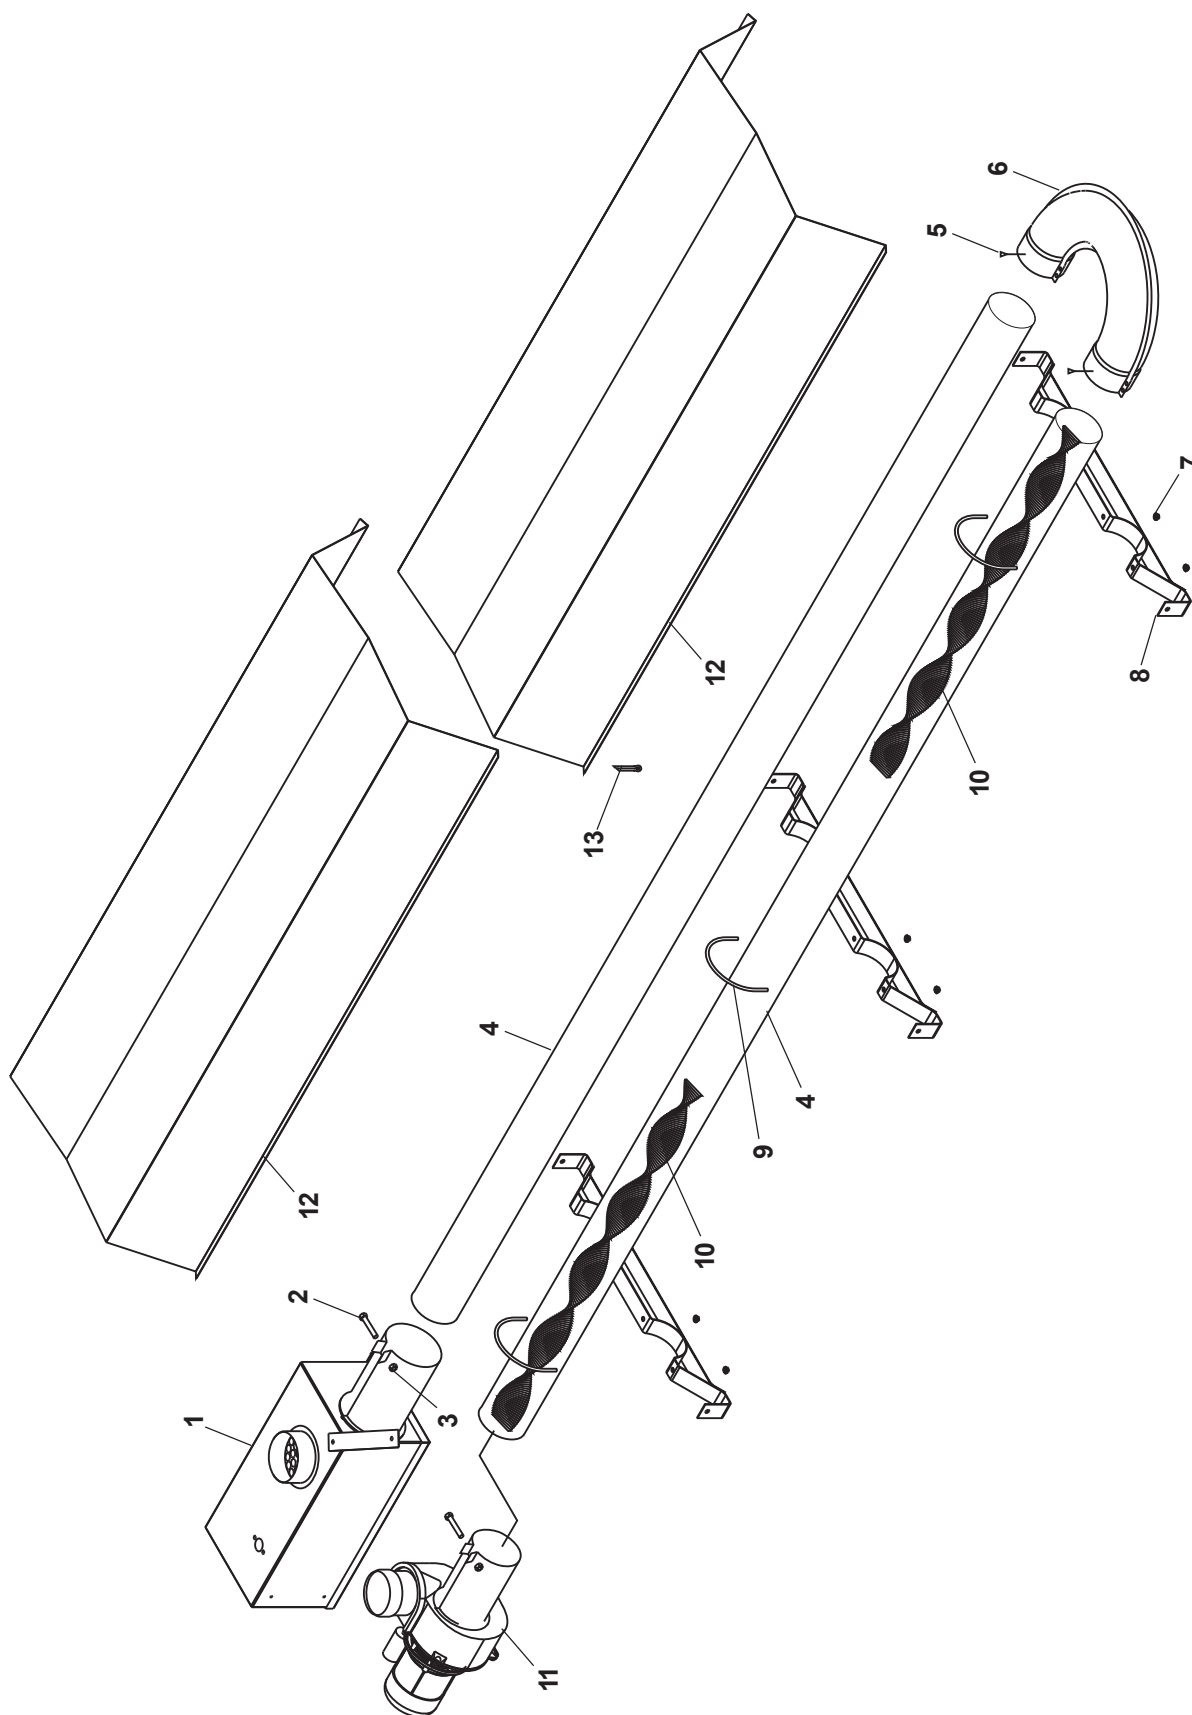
Детализовка излучающего модуля INFRA 9BL
